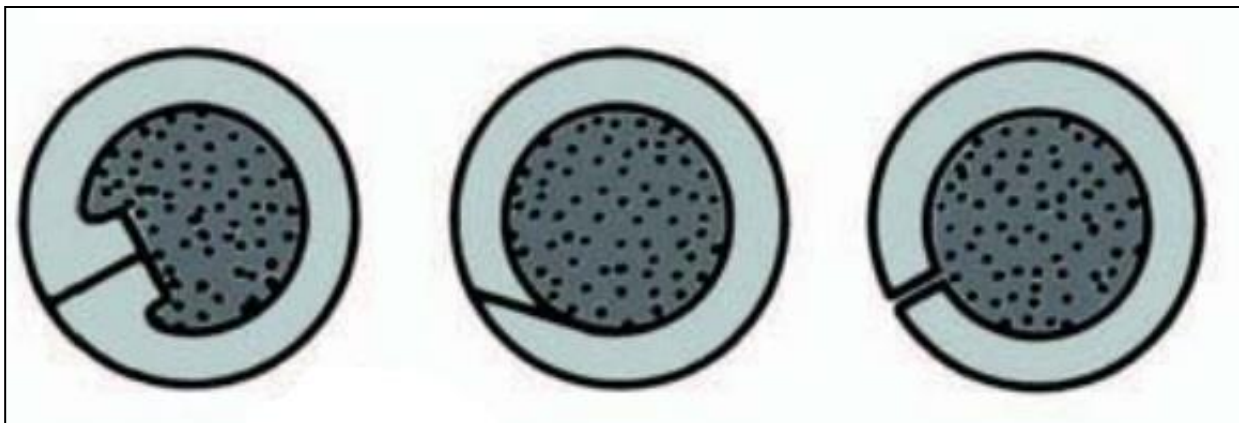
Sección Transversal De Distintas Formas De Construcción De La Soldadura FCAW [10].
